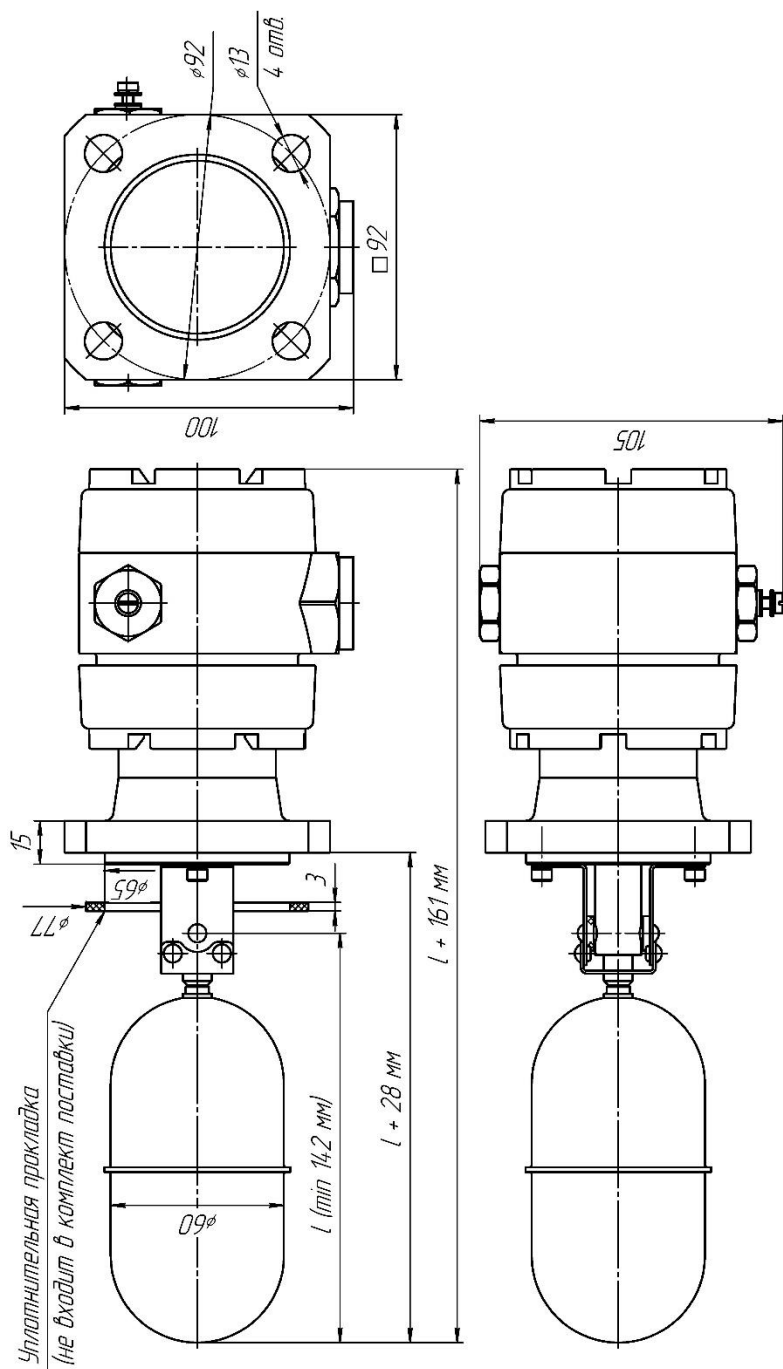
Общий вид сигнализатора уровня с присоединительным квадратным фланцем 92х92
